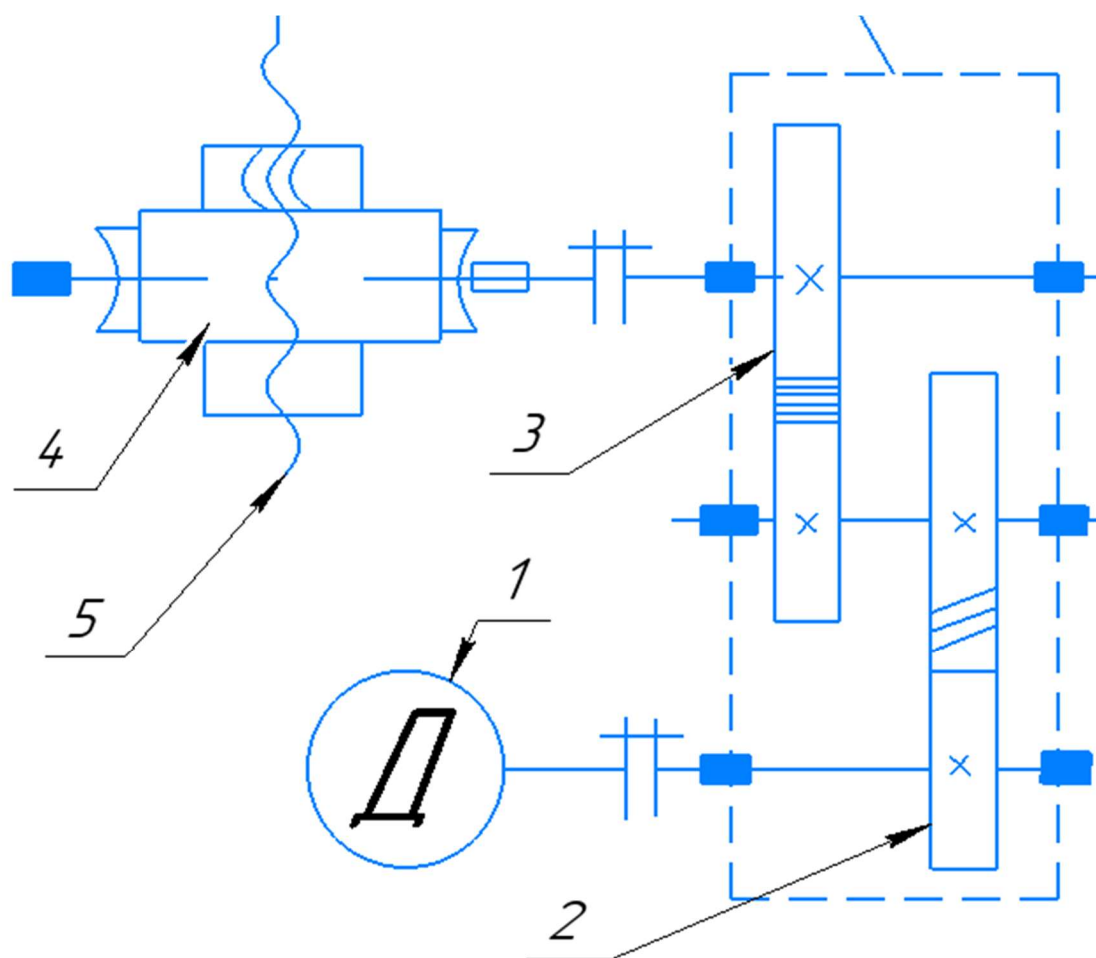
Кінематична схема приводу: 1- двигун, 2 – циліндрична косозуба передачі; 3 – циліндрична прямозуба; 4 – черв'ячна передача; 5 – гвинт.
